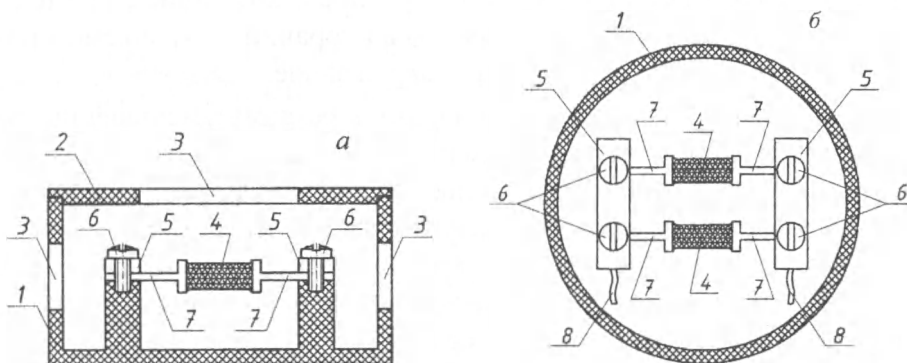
Конструкция теплового пожарного извещателя с двумя терморезисторами: а – вид спереди (в разрезе); б – вид сверху (со снятой крышкой)
